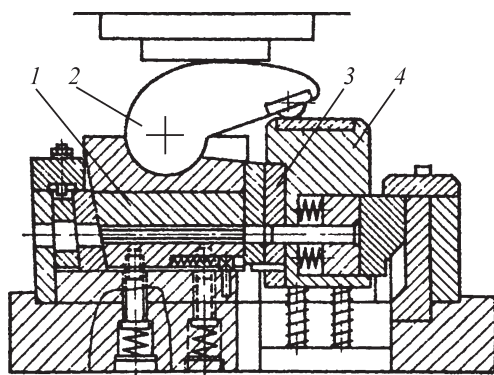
Конструктивная схема штампа для закрытой отрезки коротких заготовок от алюминиевых прутков
